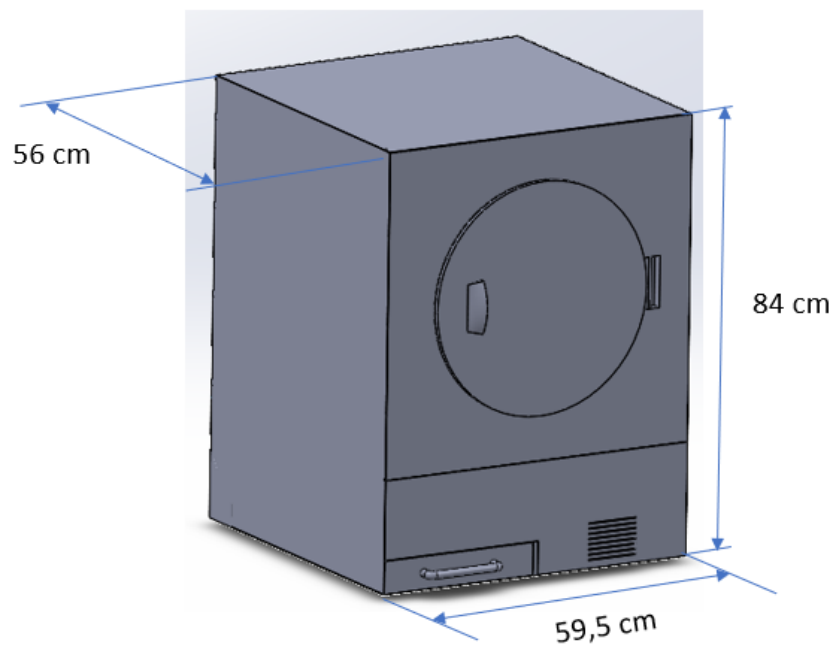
Dimensões gerais da máquina de secar roupa com bomba de calor.
